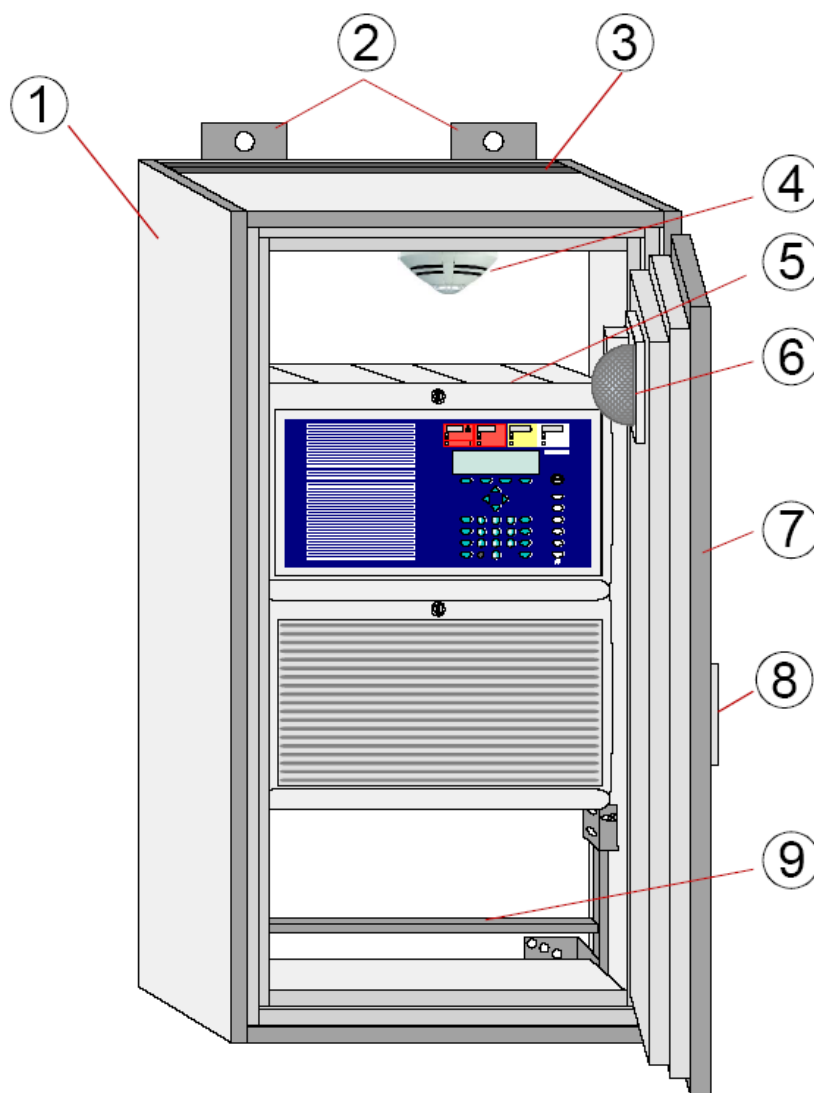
Компоновка корпуса с установленной ПКП IQ8Control M
